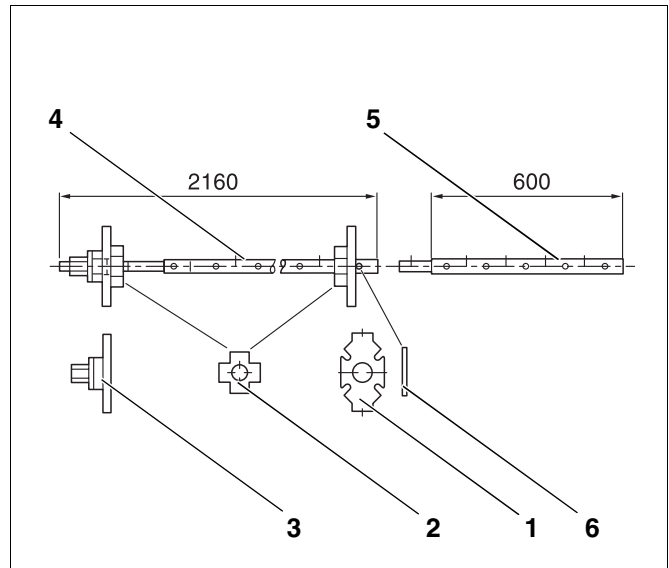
Kesselpresswerkzeug Größe 2.2 (Maße in mm)
